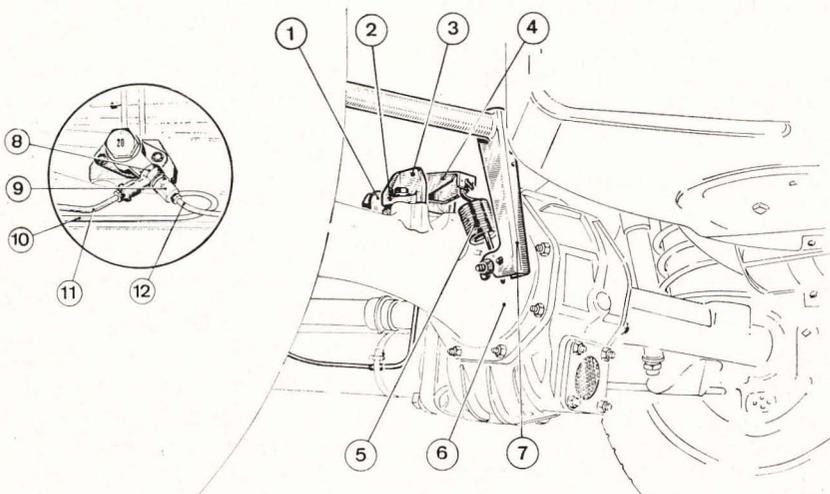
Pièces nouvelles ou modifiées depuis le montage du compensateur de freinage. 1 : compensateur de freinage (4861.05) ; 2 : support de compensateur (4872.02) ; 3 : goupille cannelée (4874.01) ; 4 : levier (4876.02) ; 5 : ressort et noix assemblés (4877.04) ; 6 : tube de pont gauche (3036.55) ; 7 : barre stabilisatrice avec crochet (5170.08) ; 8 : raccord orientable (4820.13) ; 9 : bouchon raccord (4820.13) ; 10 : tuyau intermédiaire d'alimentation des freins AR (longueur développée : 700 mm au lieu de 375 mm, 4818.28) ; 11 : tuyau d'alimentation du frein AR D. (longueur développée : 882 mm au lieu de 690 mm, 4823.20) ; 12 : tuyau d'alimentation du frein AR G. (longueur développée : 456 mm au lieu de 665 mm, 4822.26) ; cylindres récepteurs de frein AR (diamètre : 19 mm au lieu de 16 mm, 4402.21). Pièce commune à 204.
